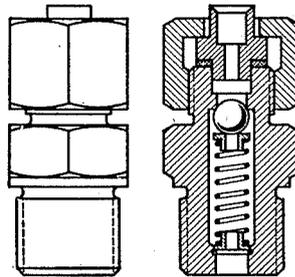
Rückschlagventil für Kolbenstangenschmierung
